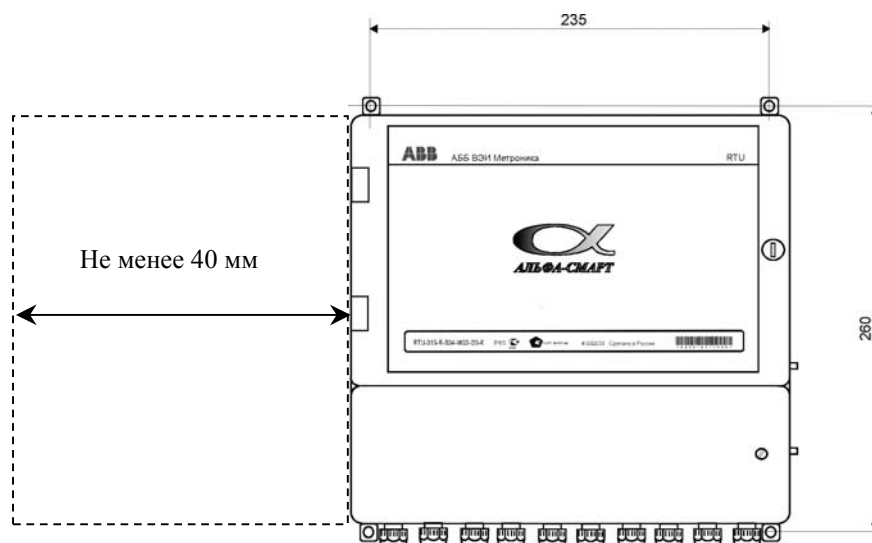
Установочные размеры корпуса УСПД типа RTU 320.
